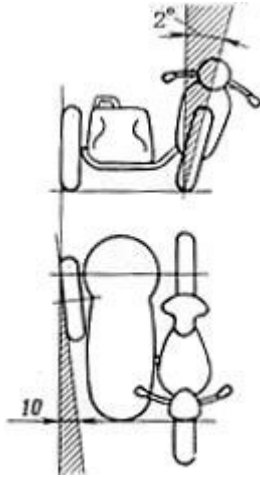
Схема регулировки развала и схождения коляски мотоцикла
